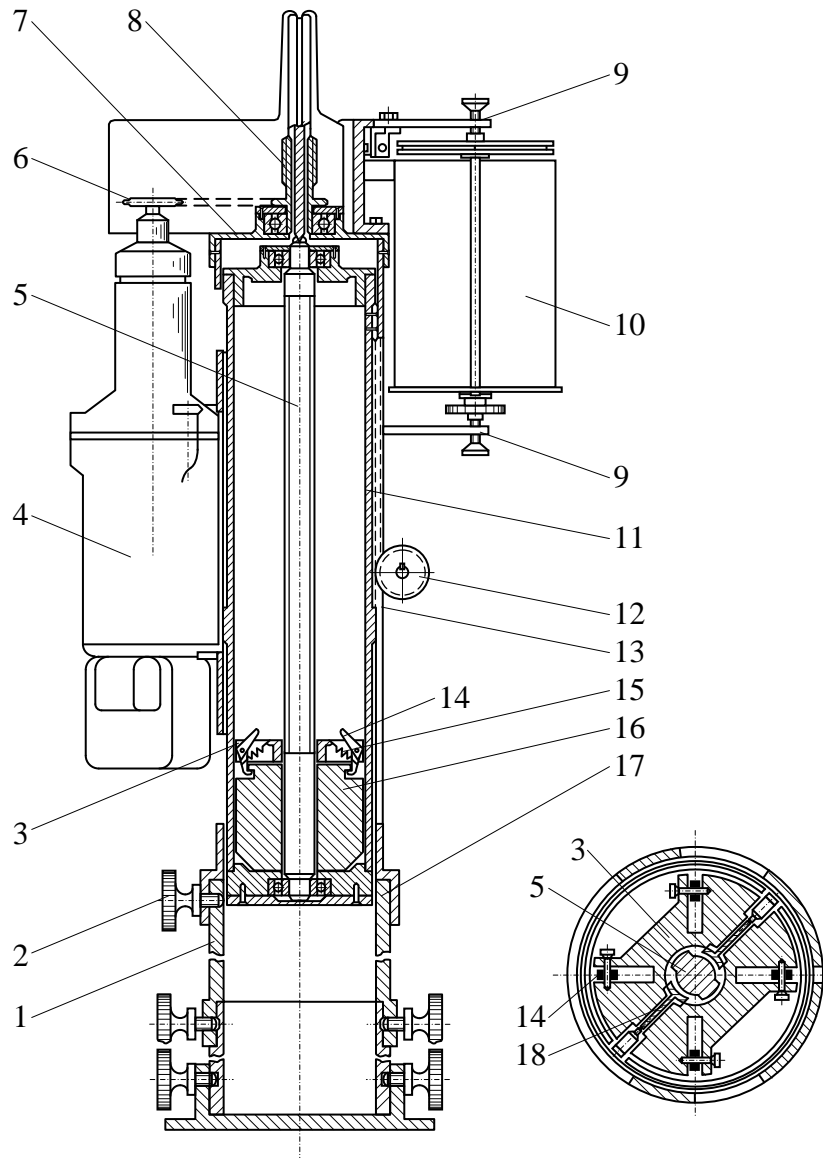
Схема переносного механізованого приладу для динамічного ущільнення ґрунтів МДУ-2: 1 – стакан для ущільнення ґрунту; 2 – затискувач; 3 – пересувна муфта; 4 – електродвигун; 5 – вал; 6 – зірочка; 7 – верхня кришка труби; 8 – черв'як; 9 – верхній і нижній кронштейни; 10 – барабан; 11 – гребінка; 12 – зубчасте колесо; 13 – напрямна труба; 14 – захват муфти; 15 – пружина захвату; 16 – вантаж; 17 – корпус приладу; 18 – штамп
